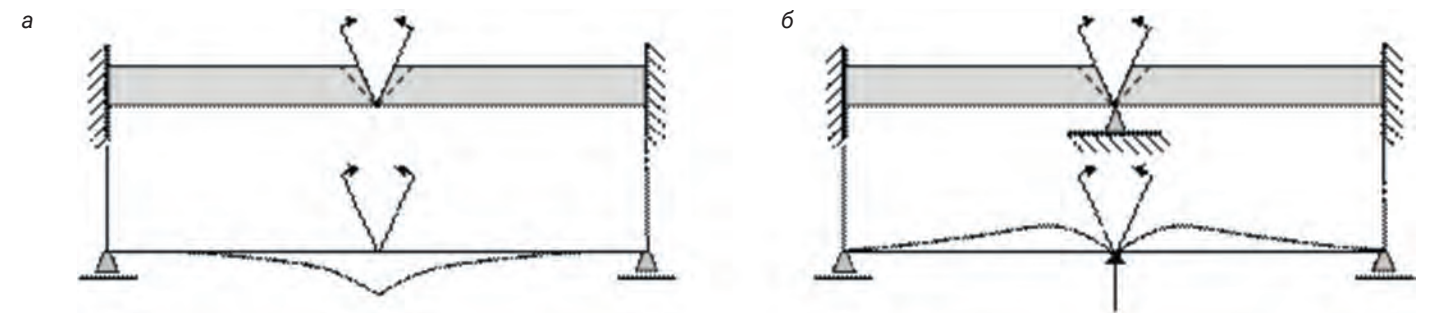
Характер деформации сварного стыкового соединения при различном закреплении:
